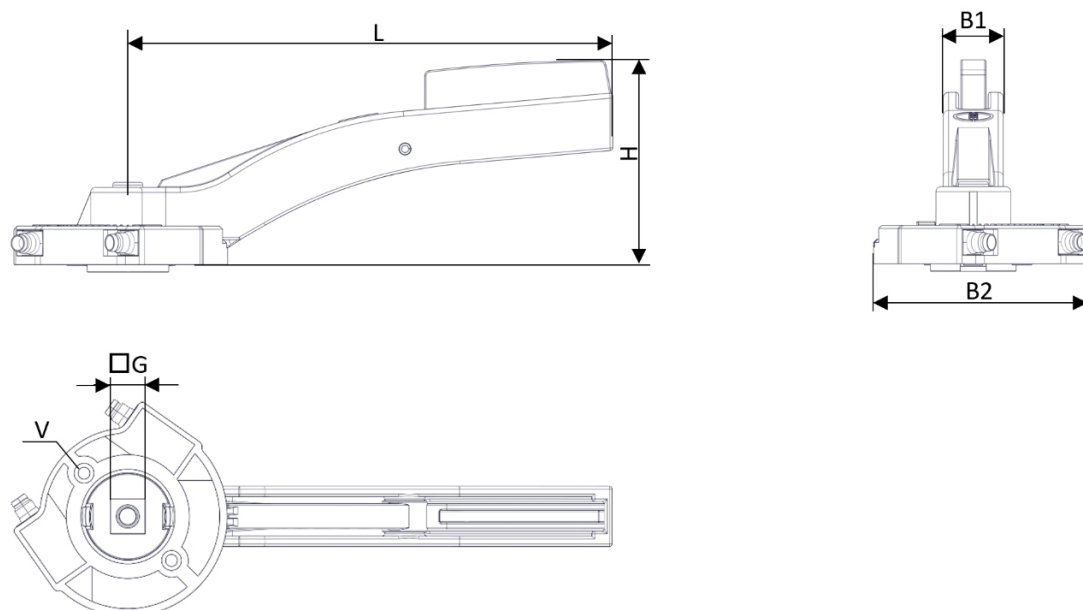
Dimensiones de la palanca de enclavamiento con sensor
